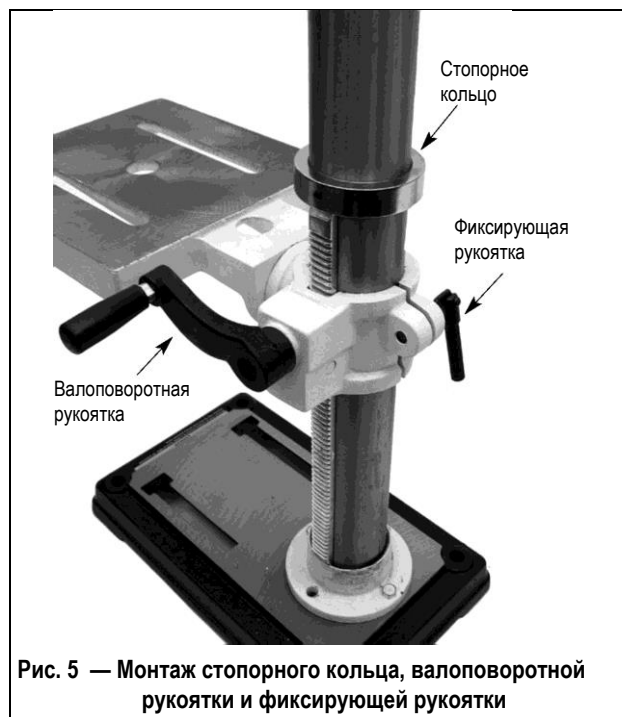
Монтаж стопорного кольца, валоповоротной рукоятки и фиксирующей рукоятки
